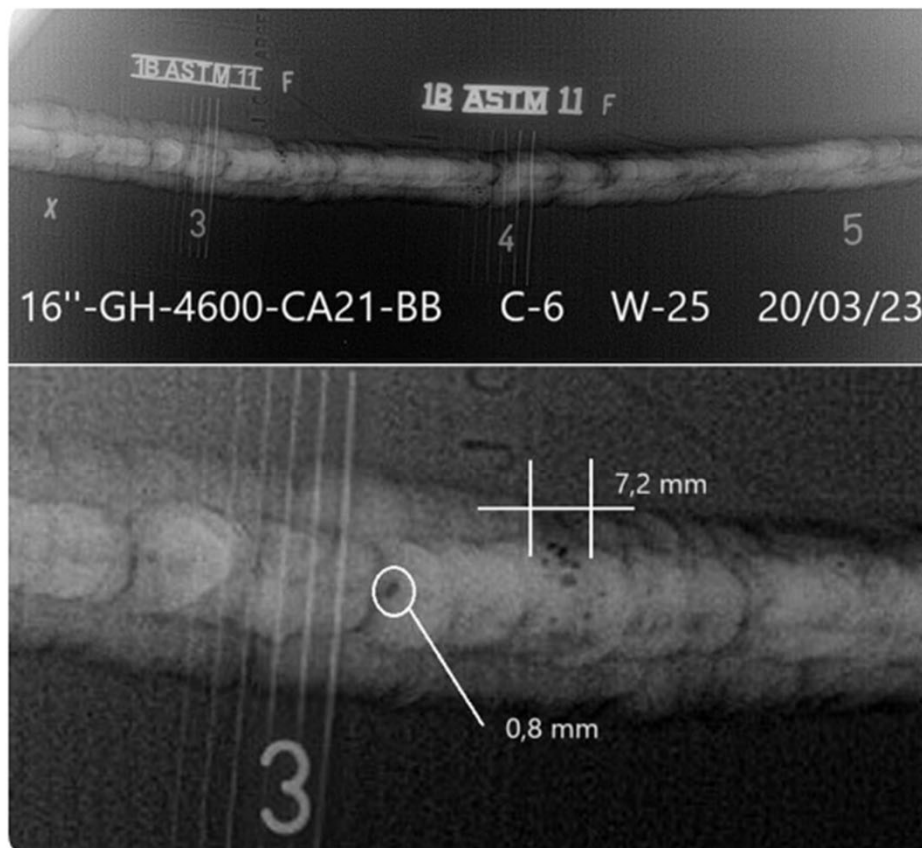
Registro de inspección de soldadura con medición por software de indicaciones
